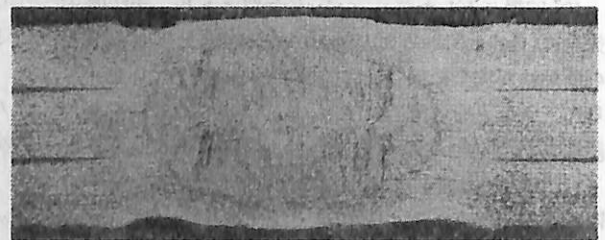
Resistance seam welded Invar joint. (文献 iii)
